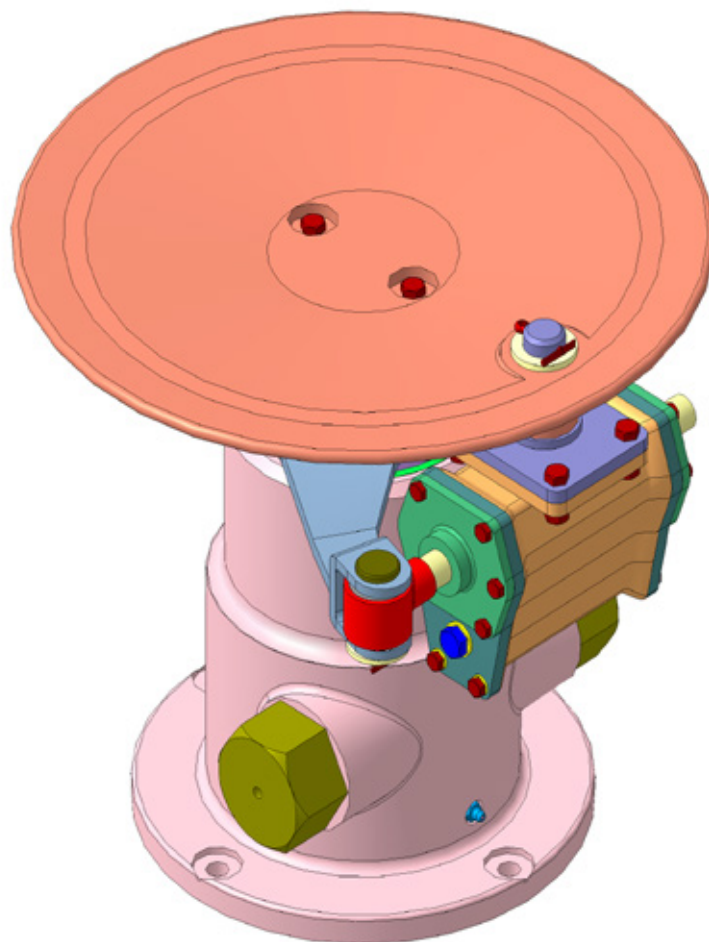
Трехмерная твердотельная модель привода стенда для проверки рулевого управления автомобилей
